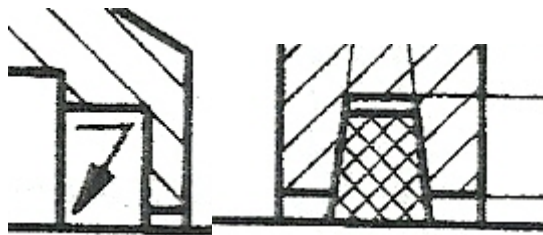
Przykład łożyska ustalającego z odpowiednim ukształtowaniem obudowy zewnętrznego pierścienia łożyska oraz pokrywy.
